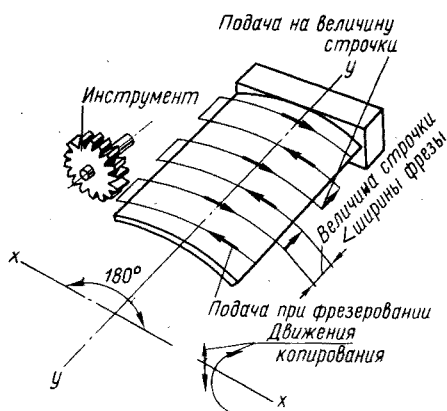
Схема фрезерования лопаток по объемному копиру на станках ОФ-31 и ОФ-33
